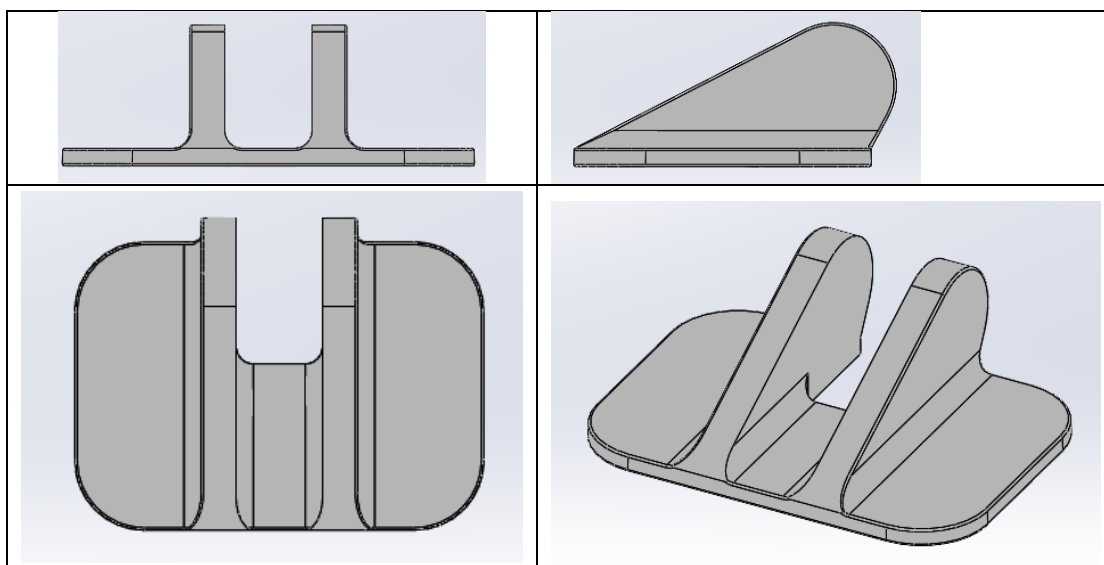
Компьютерная 3D- модель заготовки детали «Упор»
